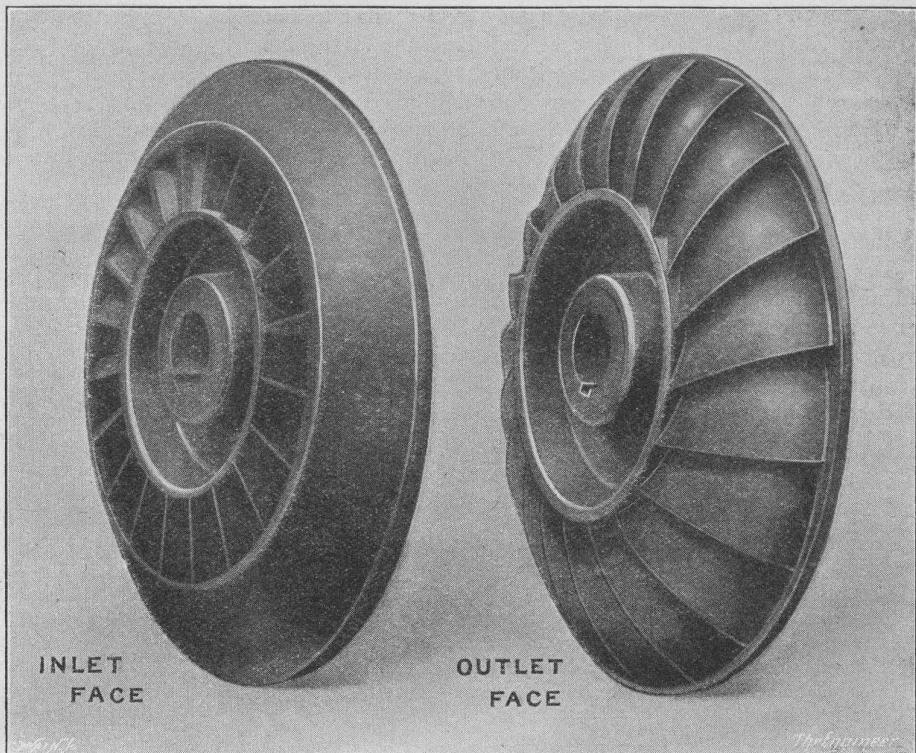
Vue des deux faces d'une roue « Turgo ».
